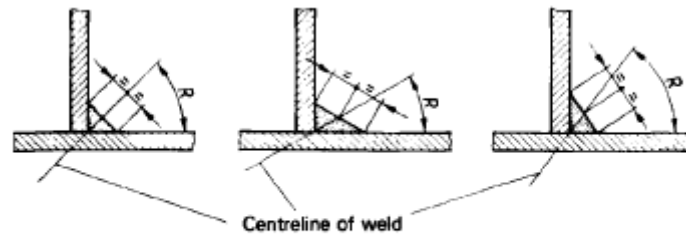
水平工件表面对称对焊焊缝的旋转 ( $R=90^\circ$ ) 范例
